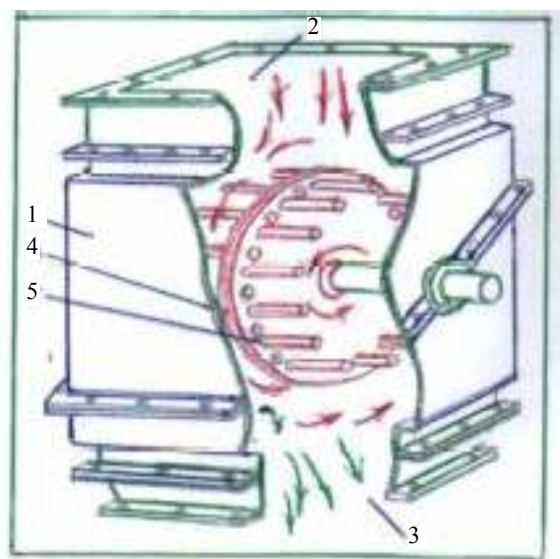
Взвихриватель: 1 – корпус; 2 – вход закладочной смеси; 3 – выход смеси; 4 – ротор; 5 – штифты
